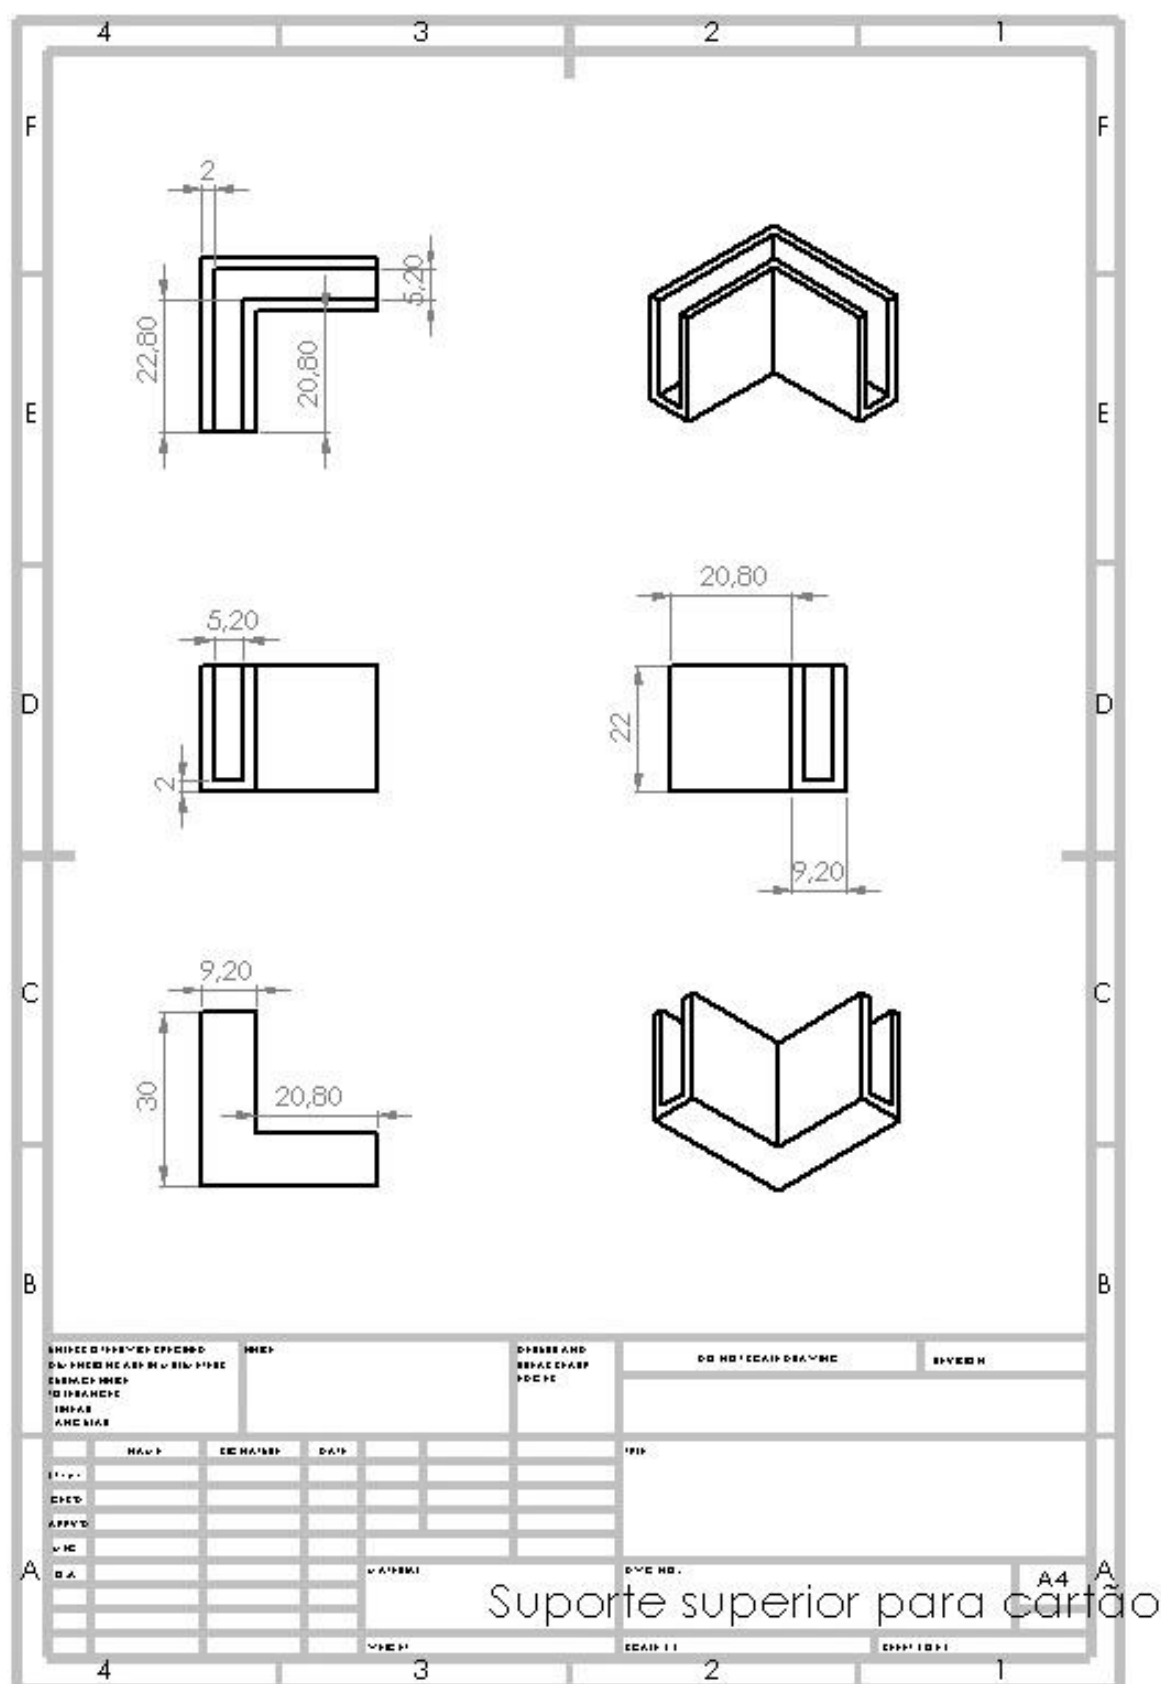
Desenho técnico da peça Suporte superior para cartão
